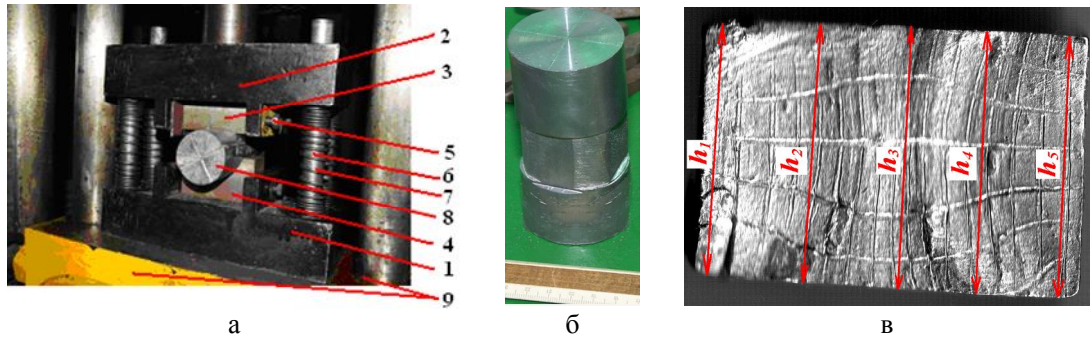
Штамповый блок для исследования протяжки заготовок (а), деформированный образец (б), вырезанный темплет и замер высот (в): 1 и 2 – нижняя и верхняя плиты; 3 и 4 – верхний плоский и нижний вырезной бойки; 5 – крепёж; 6 и 7 – направляющие и пружины; 8 – образец; 9 – испытательная машина
